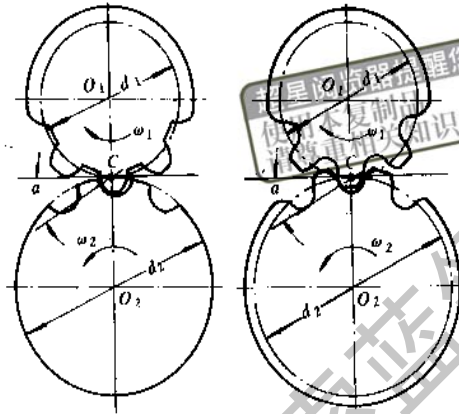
单圆弧齿轮传动 图 13-3 双圆弧齿轮传动
